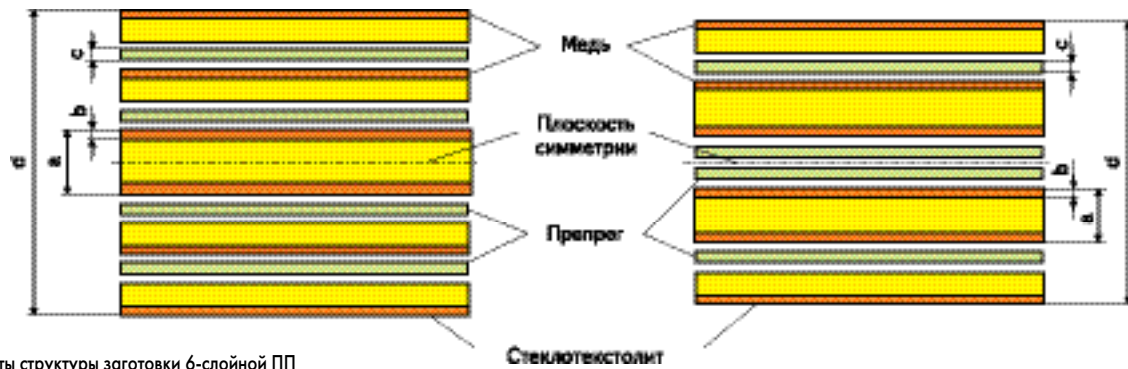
Варианты структуры заготовки 6-слойной ПП
